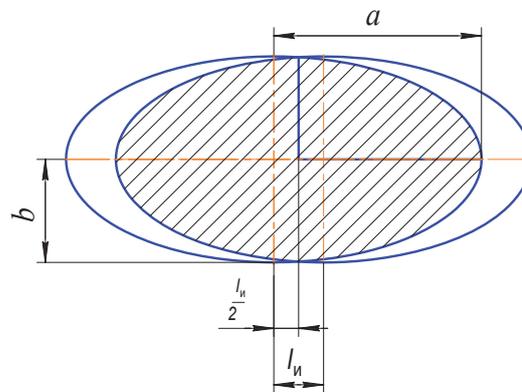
Геометрические параметры сварочной точки эллиптической формы
